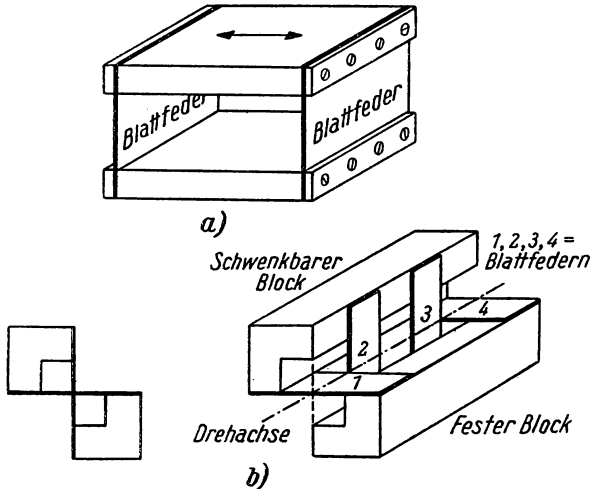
Federführungen. a) Blattfederanordnung für parallelgeführte Bewegung. b) Gekreuzte Federn gestatten Drehung um eine Achse
